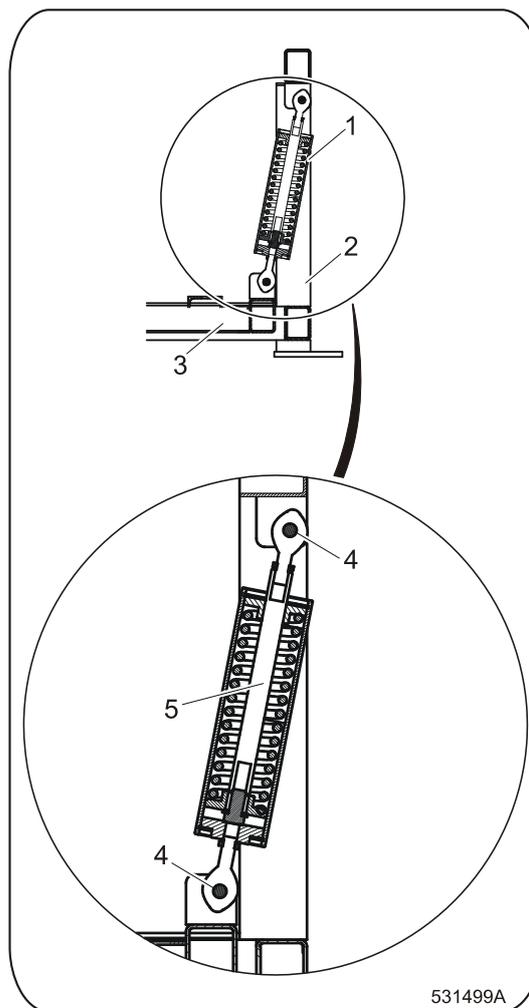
B Máquinas 80-100-120 kg / 180-230-275 lbs
